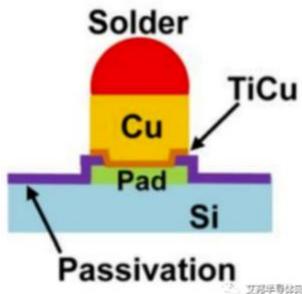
, Cu+Solder 统称为bump, 细分又可以分为Cu bump 和Solder Bump. 当然Solder bump是植在铜柱(Copper bump)上的。如图2所示, 当copper bump pitch 小于10~20um时, 焊锡球 solder bump就变成了工艺难点及缺陷的主要来源。这时候就需要一种新的工艺来解决bump 间距小于10微米芯粒间键合的问题。当然Hybrid Bonding在电学性能方面也有独特的优势, 如图3所示, Hybrid Bonding信号丢失率几乎可以忽略不计, 这在高吞吐量, 高性能计算领域优势明显。在业界强烈需求的呼唤下, Hybrid Bonding腾空出世。
